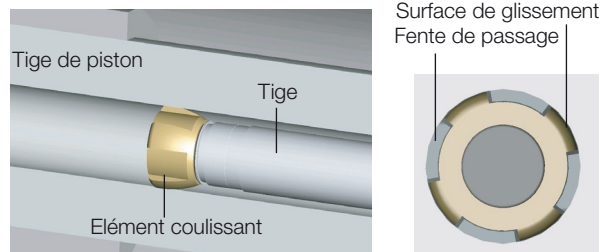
Vue détaillée et vue de dessus de l'élément coulissant
